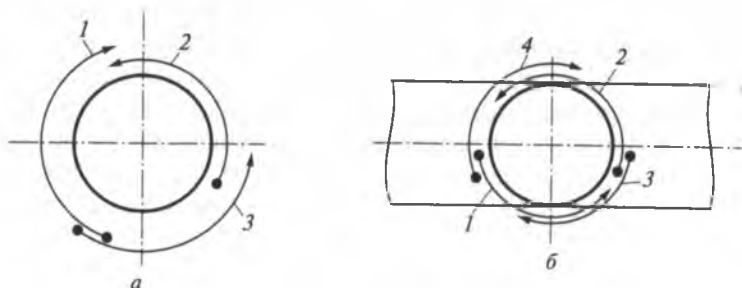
Схема сварки неповоротных стыков трубы *a* и последовательность наложения швов при сварке отростка с трубой *б*:
